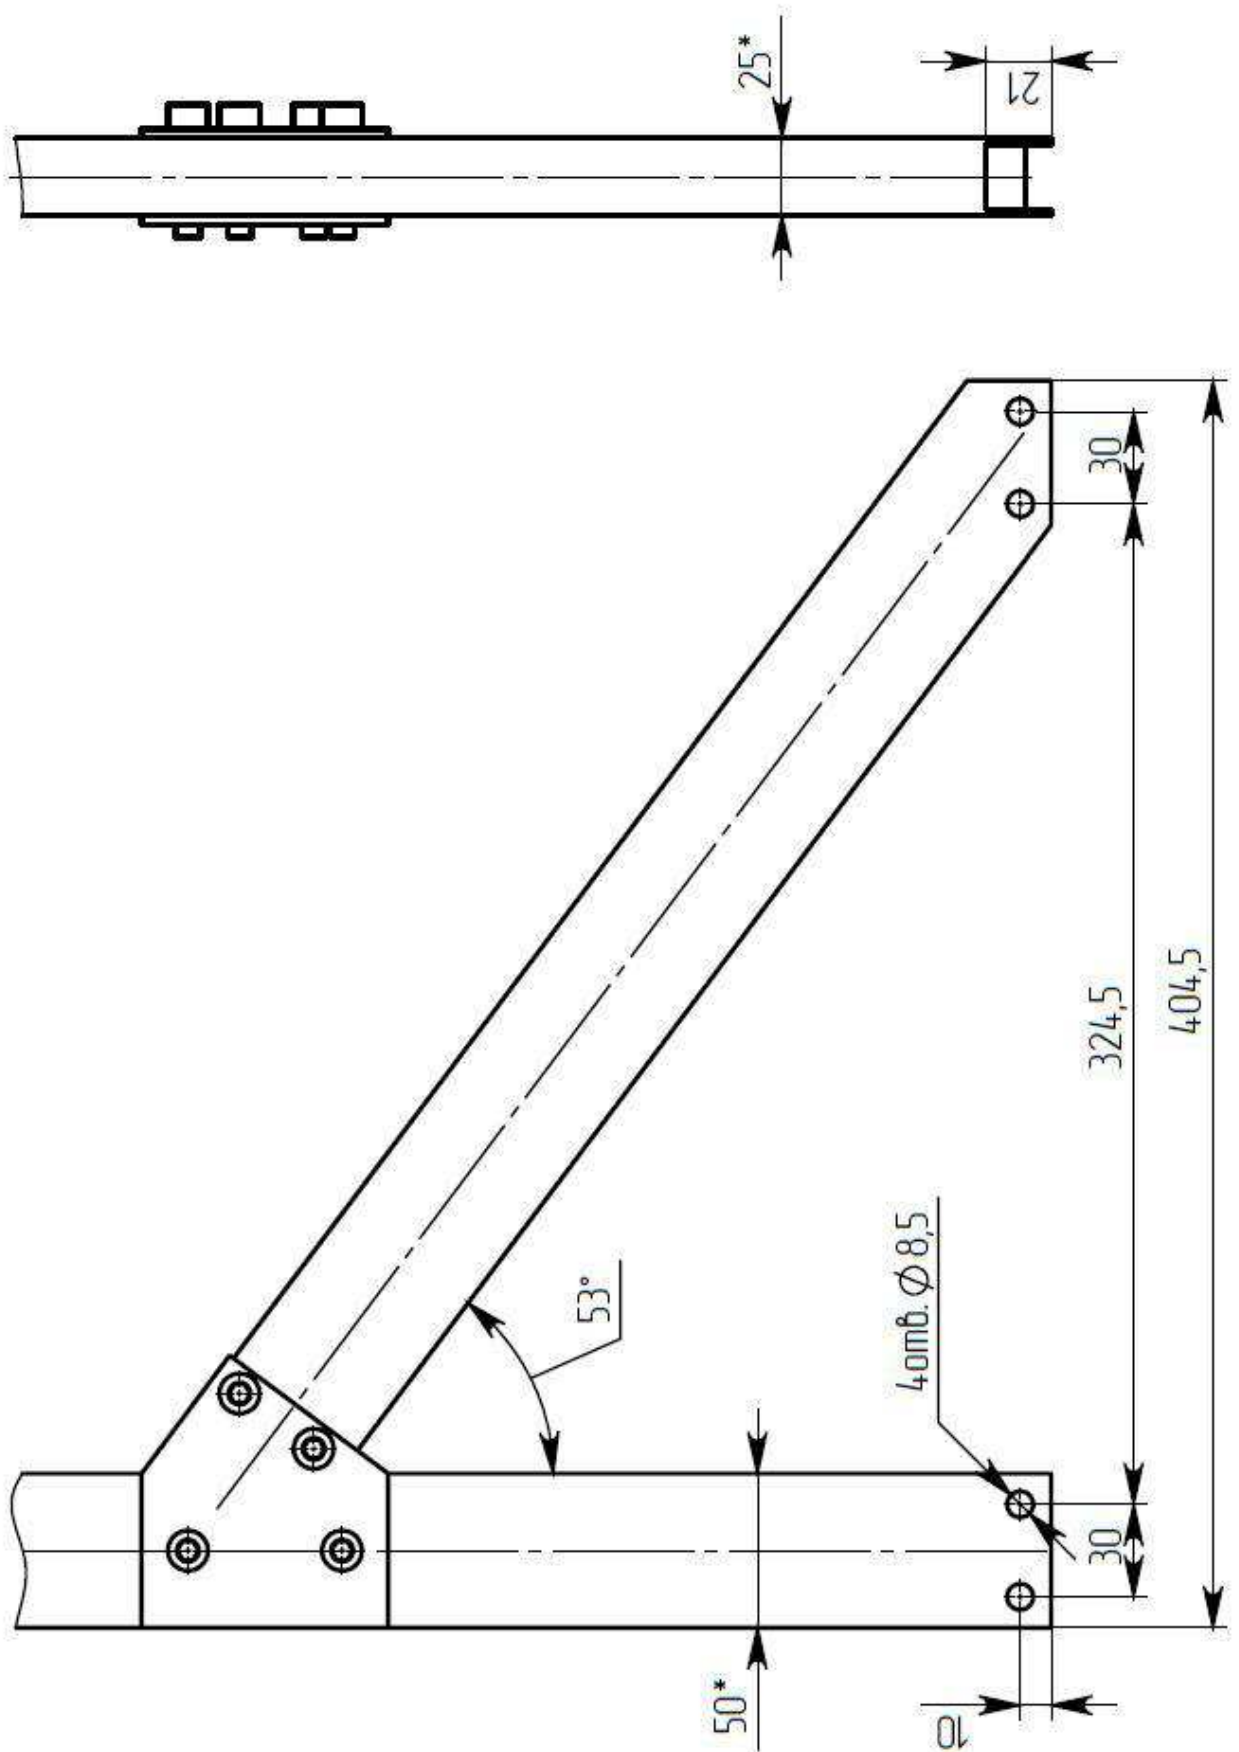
Разметка штанги 50x25 мм для крепления моноблока
